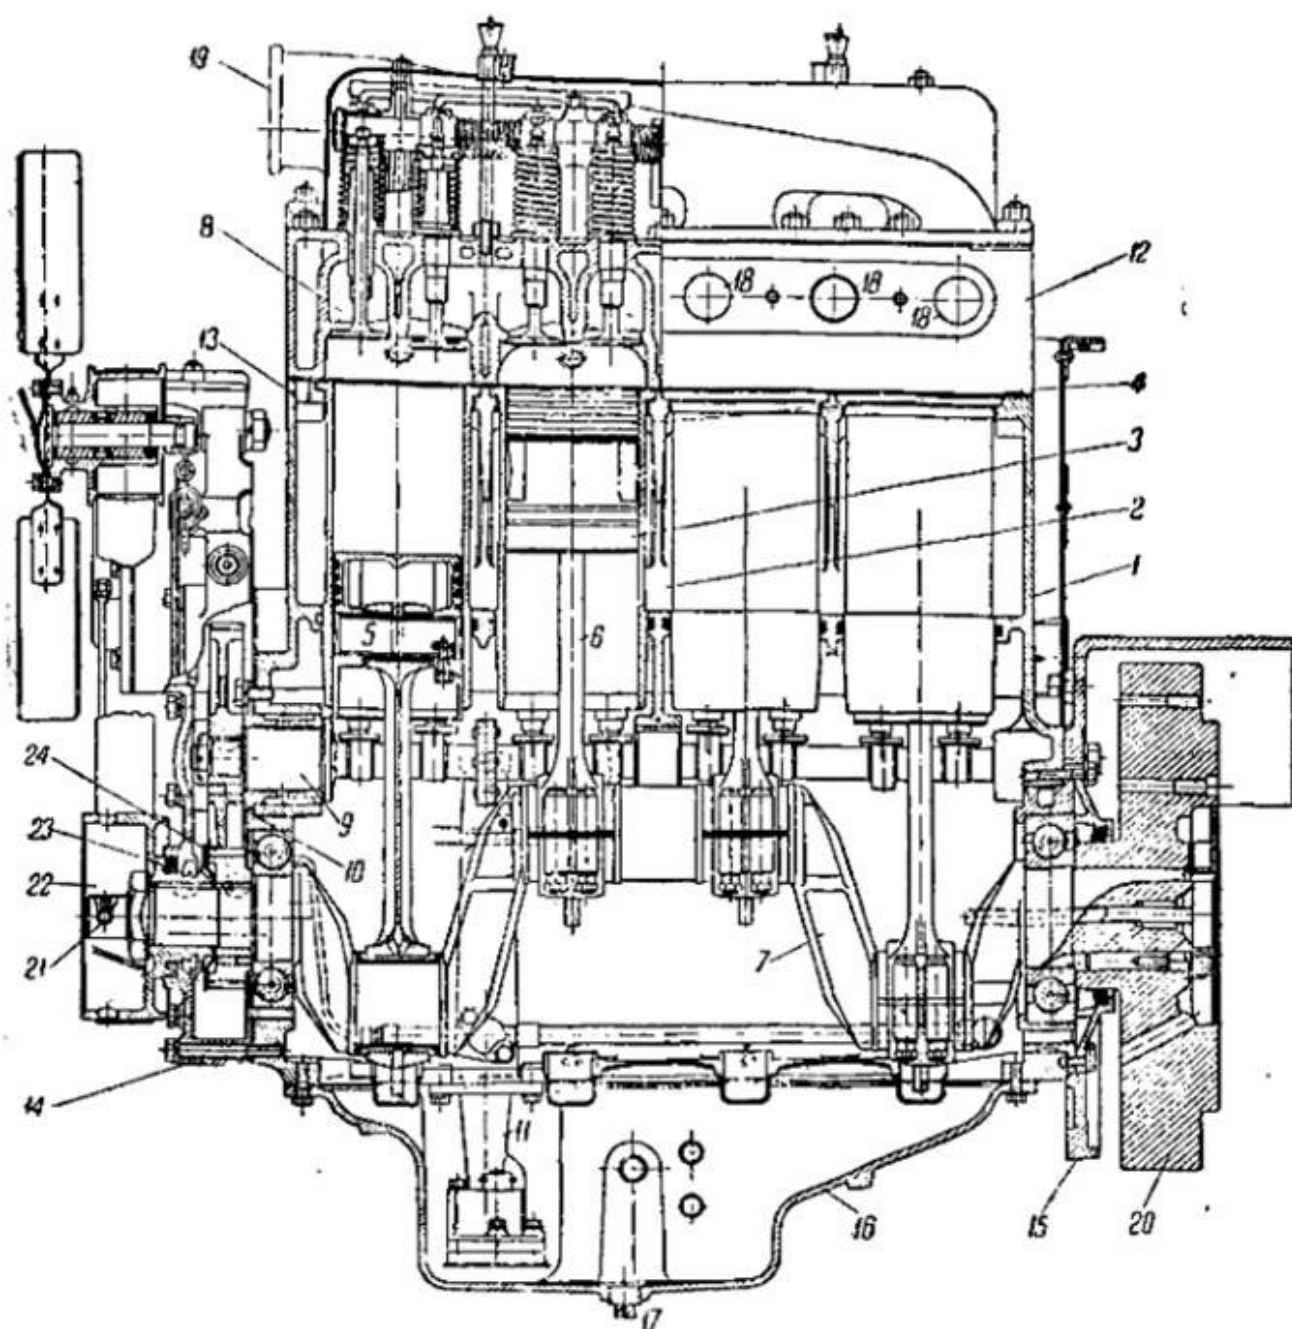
1 — блок-картер; 2 — гильза цилиндра; 3 — поршень; 4 — поршневое кольцо; 5 — поршневый палец; 6 — шатун; 7 — коленчатый вал; 8 — клапан; 9 — распределительный вал; 10 — распределительная шестерня; 11 — масляный насос; 12 — головка цилиндров; 13 — прокладка головки цилиндров; 14 — передняя балка мотора; 15 — задняя балка мотора; 16 — нижняя крышка картера; 17 — спускная пробка; 18 — всасывающие и выхлопные окна; 19 — отводящий водяной патрубок; 20 — маховик; 21 — штифт для захвата пусковой рукоятки; 22 — нижний шкив вентилятора; 23 — сальник нижнего шкива вентилятора; 24 — маслоотражательная шайба.
